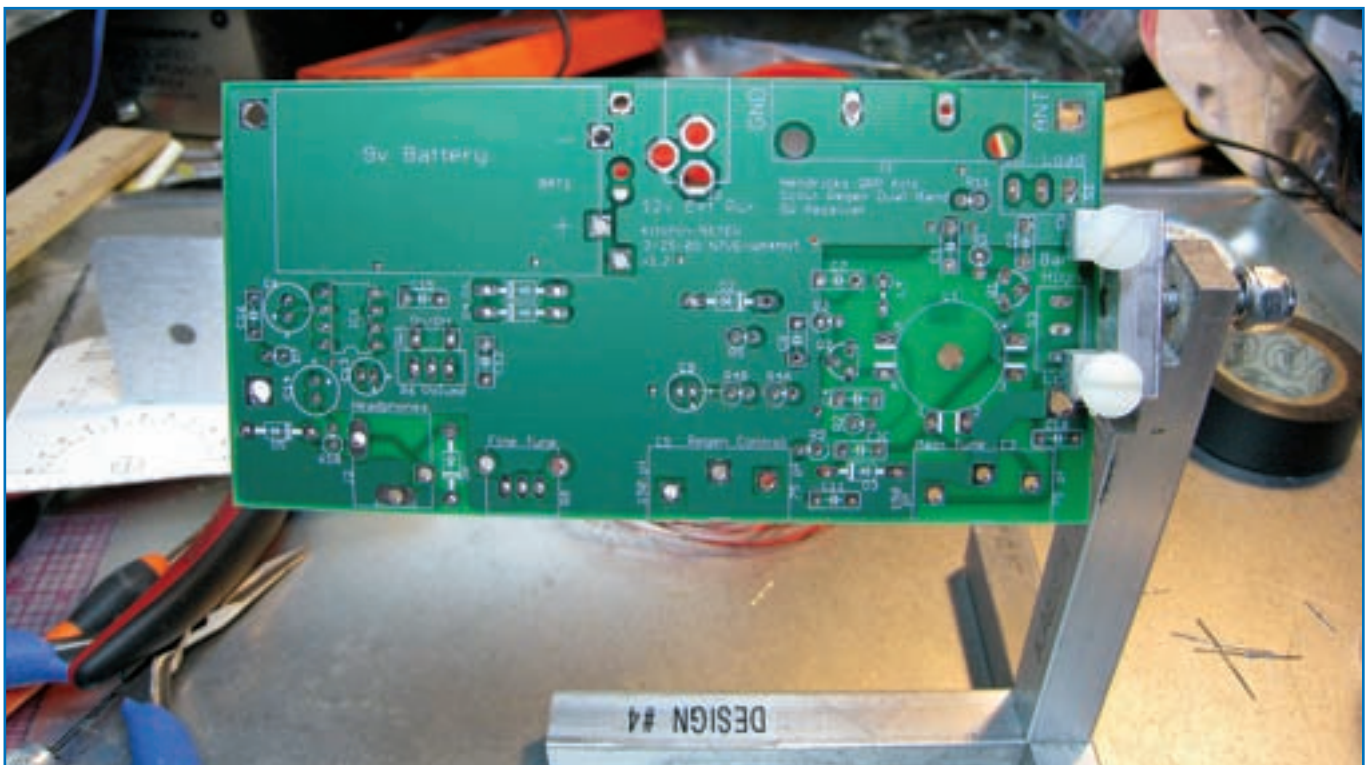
Foto C.- La placa de circuito impreso del kit Scout Regen de Hendricks es de doble cara, con agujeros estañados que facilitan la soldadura de los componentes.
